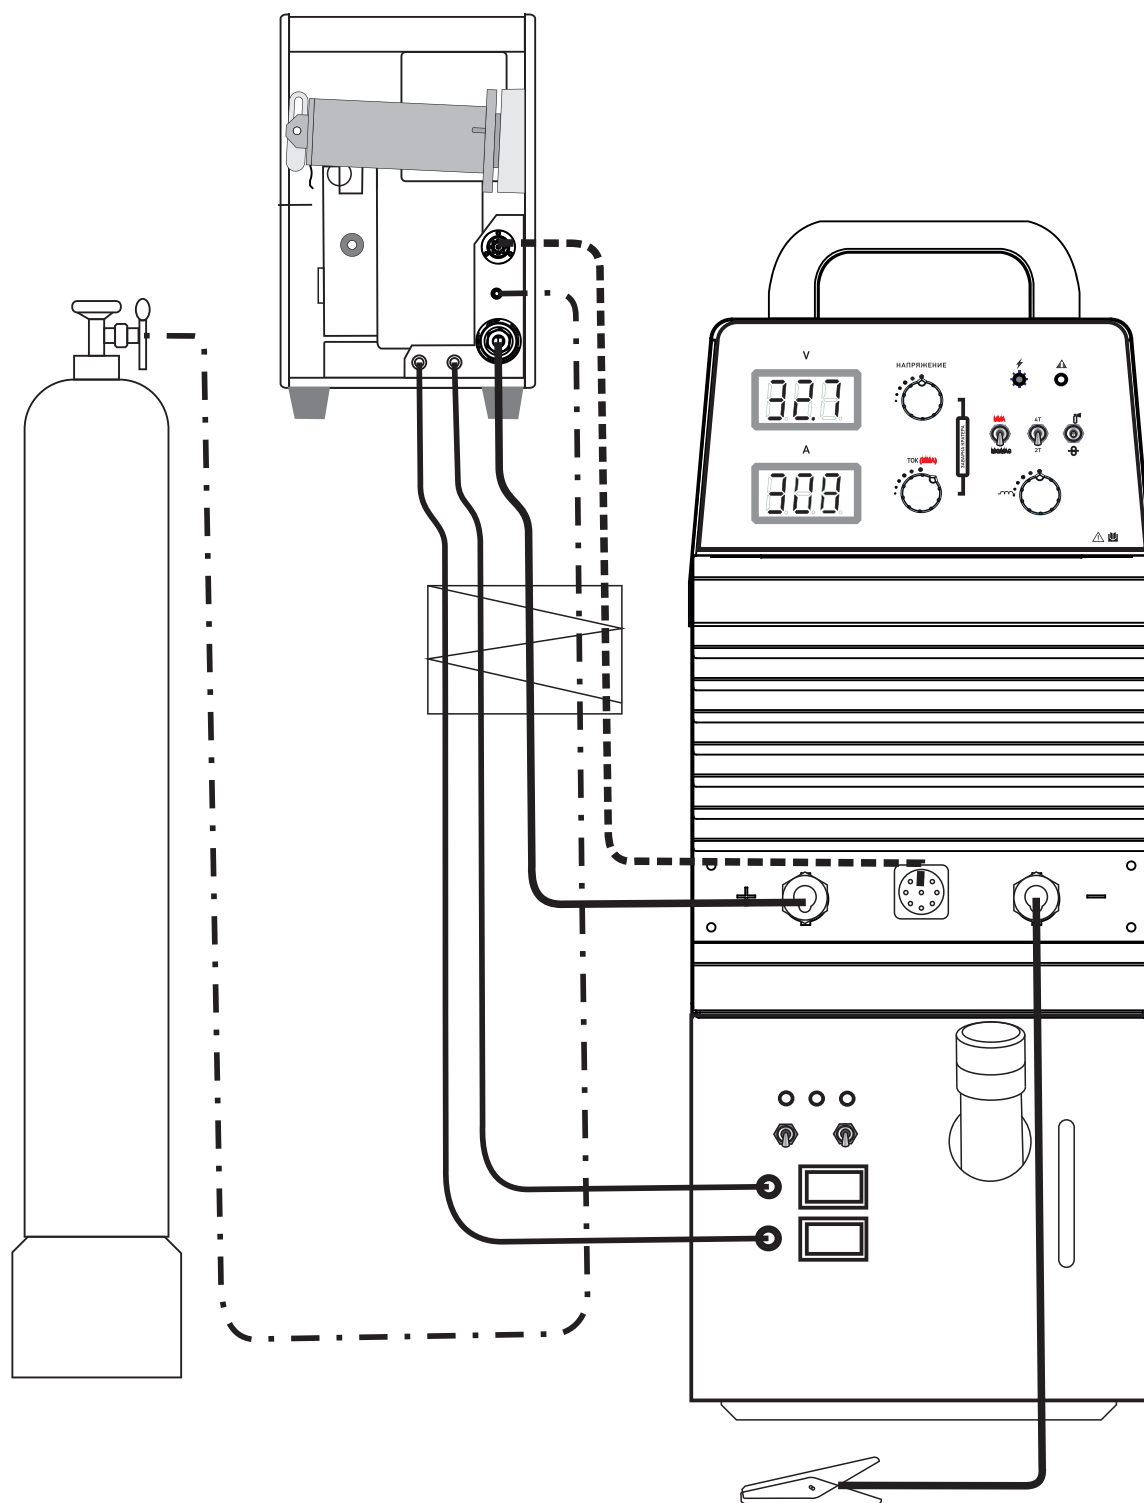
Схема подключения механизма подачи сварочной проволоки и БВО
